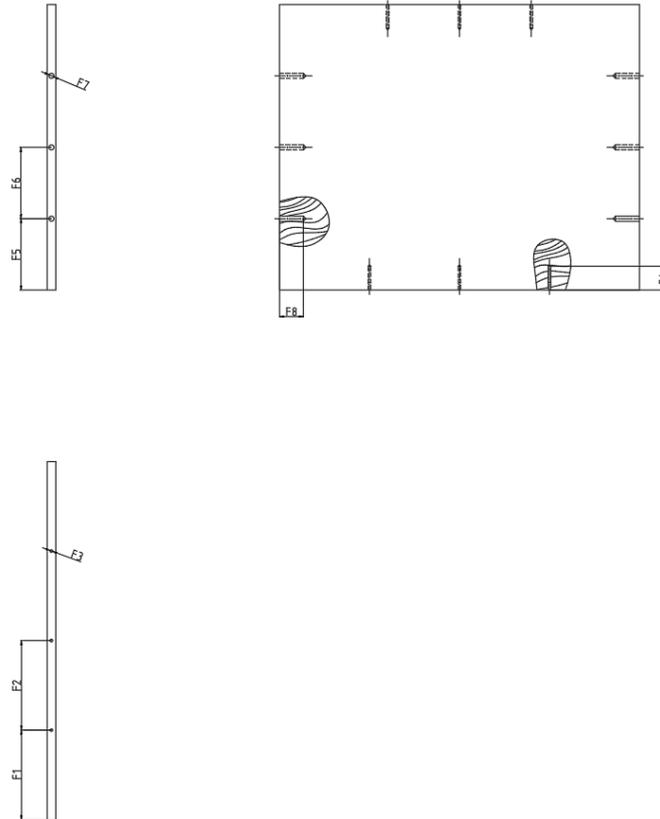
Plano Dimensionado Previo de la Vertical interior 1.1.5
